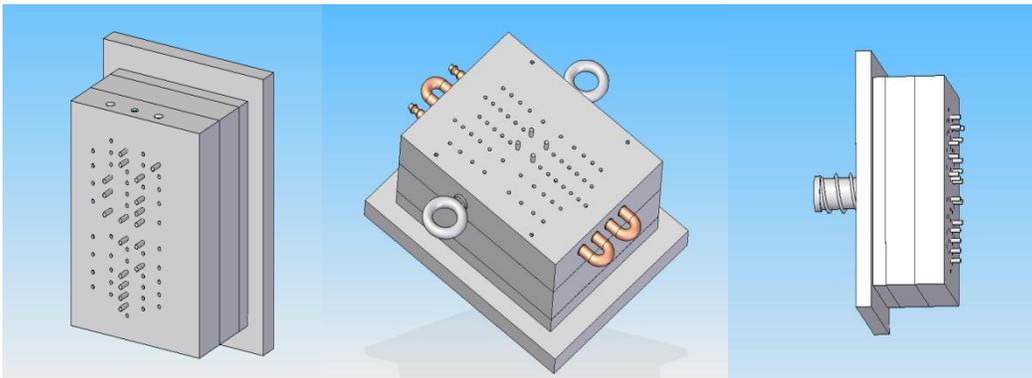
Diseño inicial del portamolde con placa de soporte y de expulsores universales.
